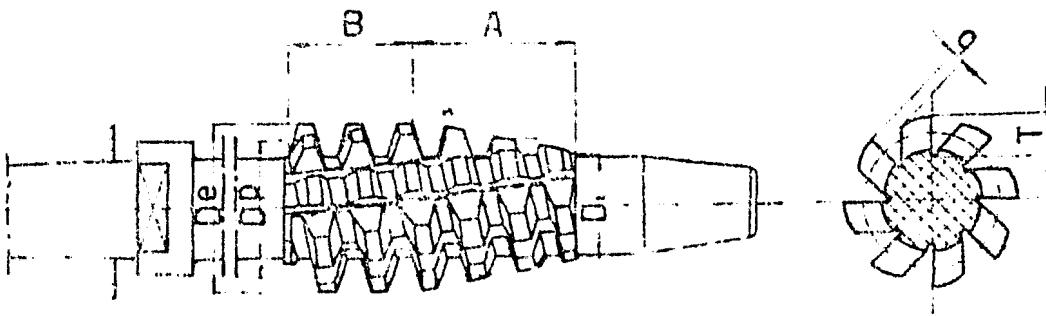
Fresa-tornillo para el tallado de dientes helicoidales de ruedas cilíndricas.
